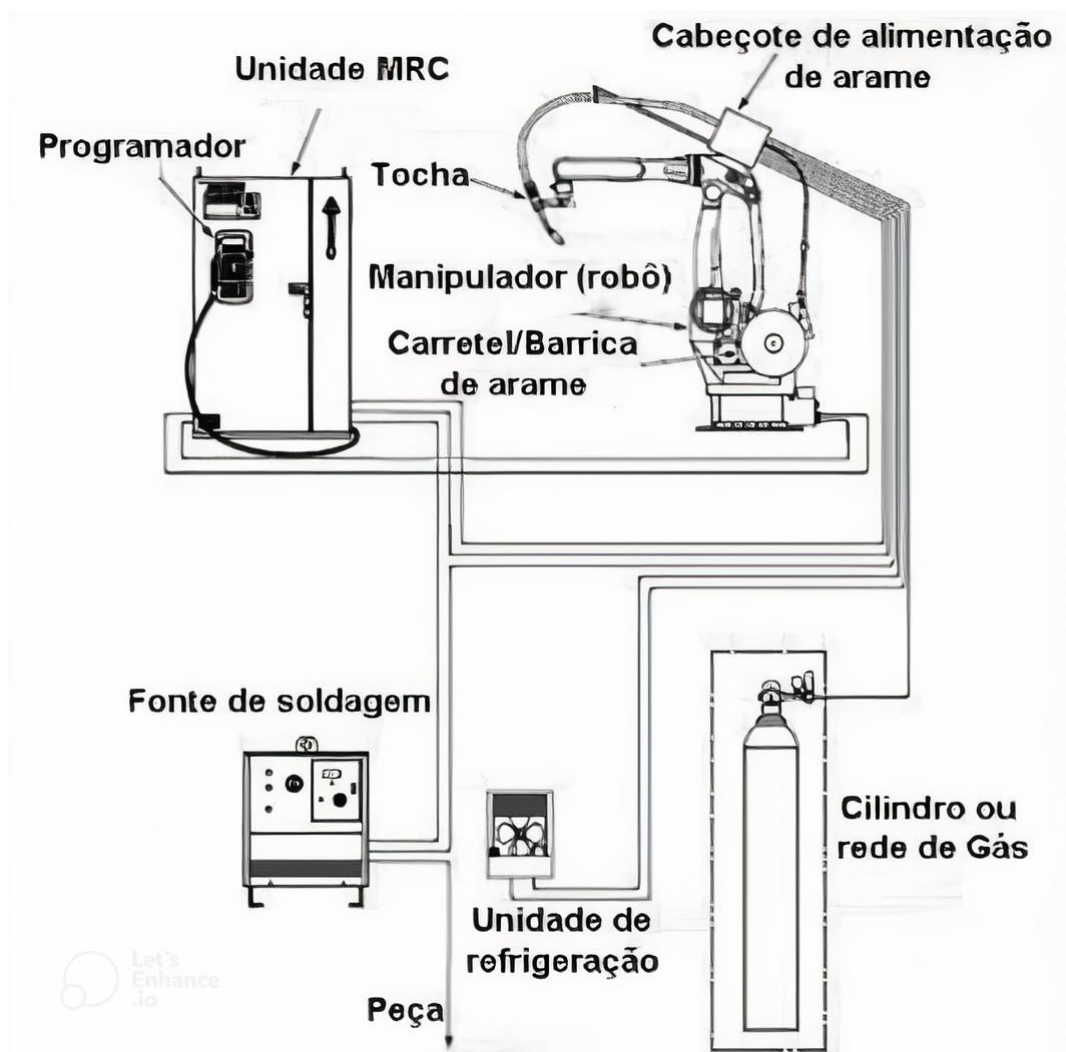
Representação esquemática de parte dos componentes de uma célula de soldagem robotizada [11].
